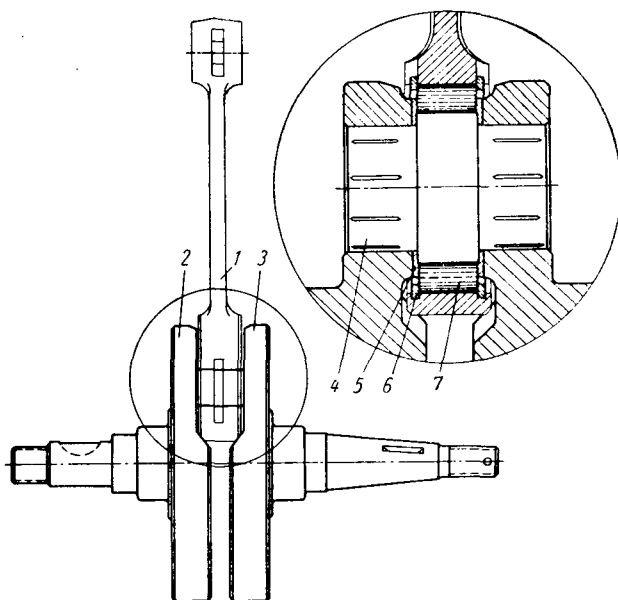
Коленчатый вал двигателя мотороллеров ВП-150 и В-150М в сборе:
